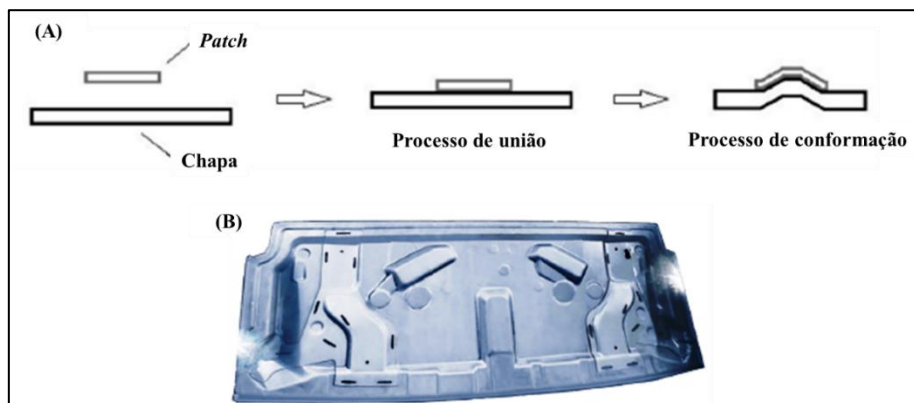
Patchwork Blanks (A) etapas de conformação e (B) exemplo de componentes obtidos por meio dessa técnica.
